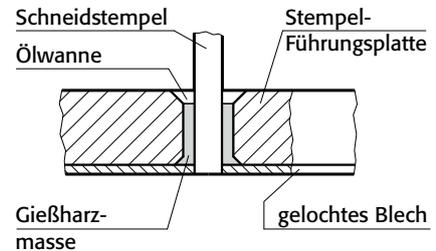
Vergossener Schneidstempel für schnellaufende Werkzeuge.
